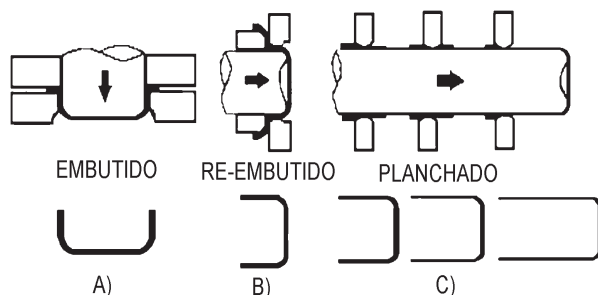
Fabricación de latas de aluminio por estirado y planchado.
